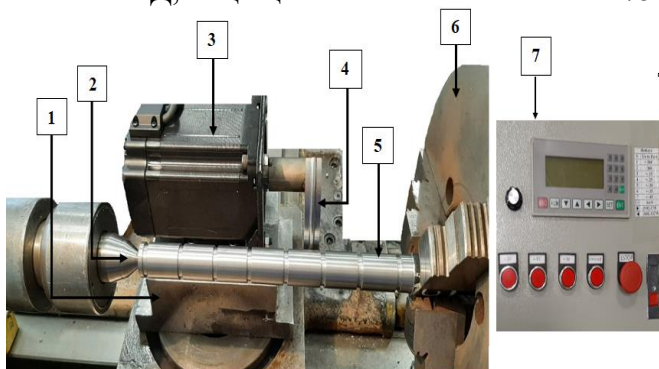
Общий вид устройства для маятникового ППД наружных поверхностей цилиндрических деталей:
